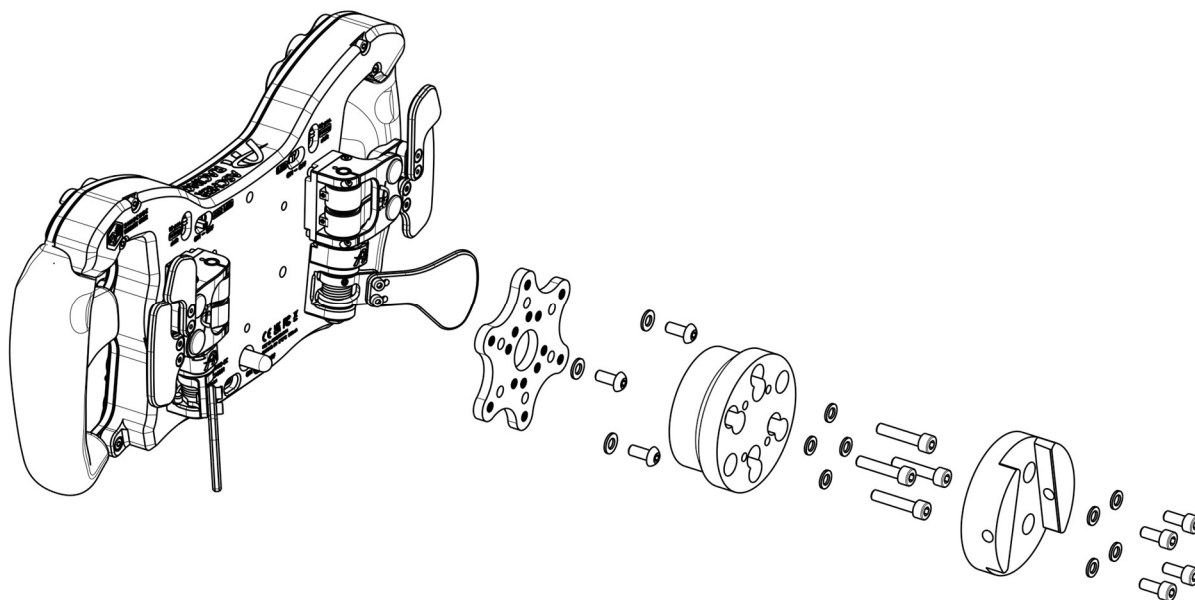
Montage des SC2 SQR WHEEL SIDE – Simucube Adapter
